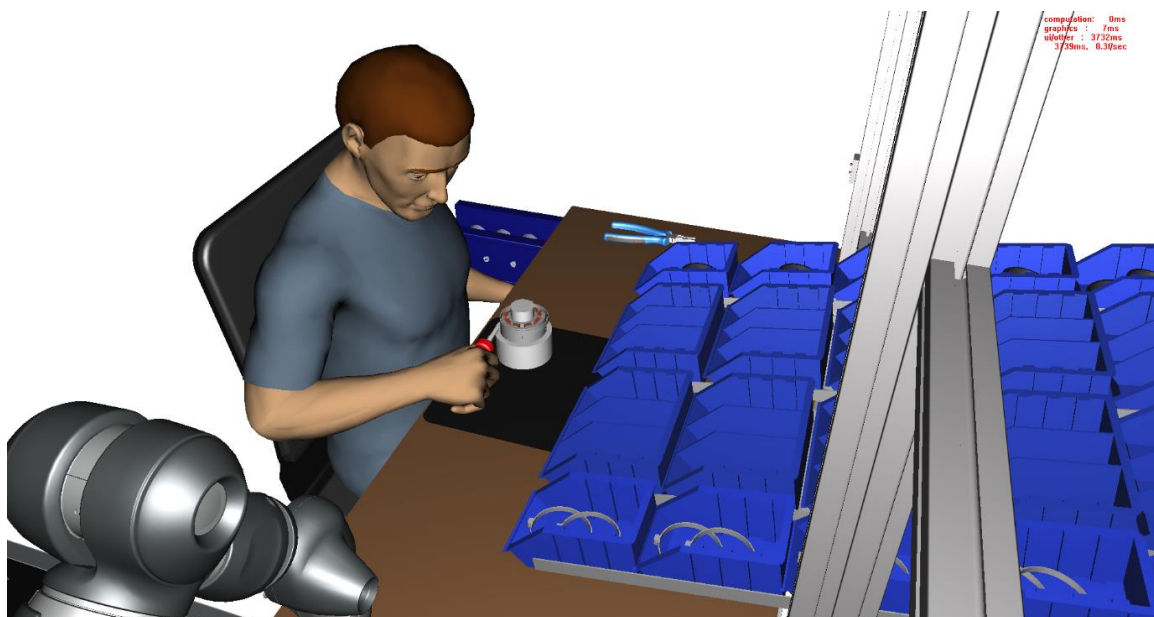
Operace 240: Umístění segmentu do přípravku na oporu tvaru statoru
